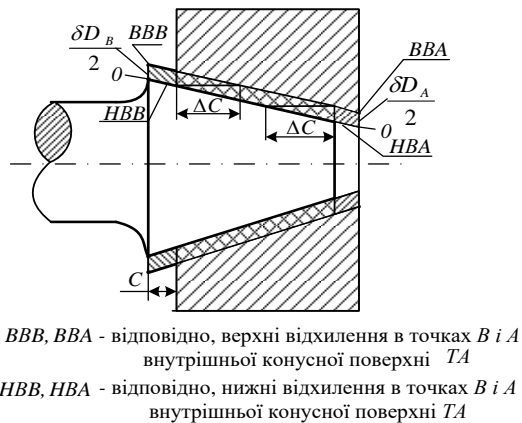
Схема полів допусків на діаметри конусних деталей ТА
